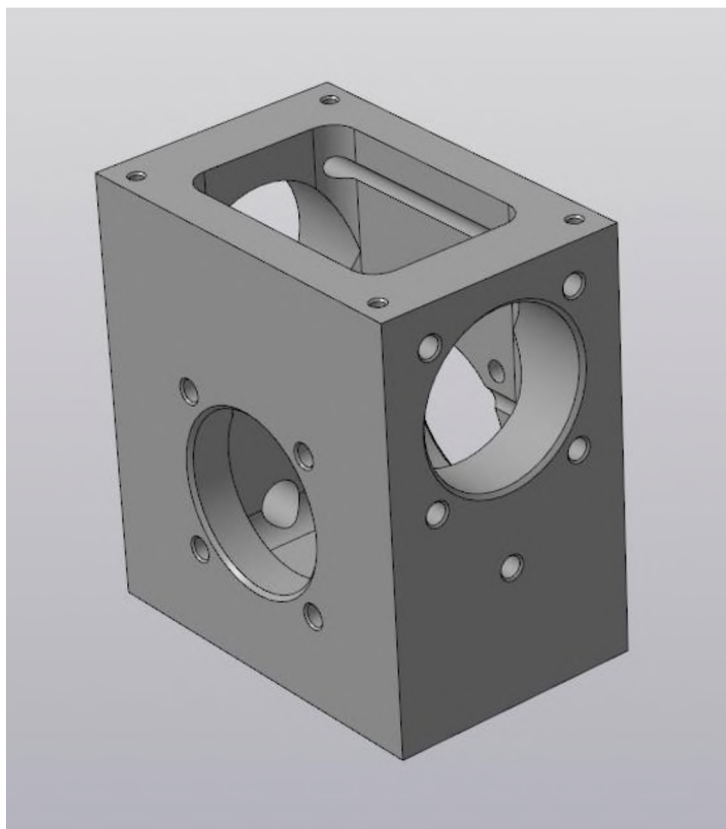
3D модель деталі «Корпус». Ізометрія, вигляд зверху
